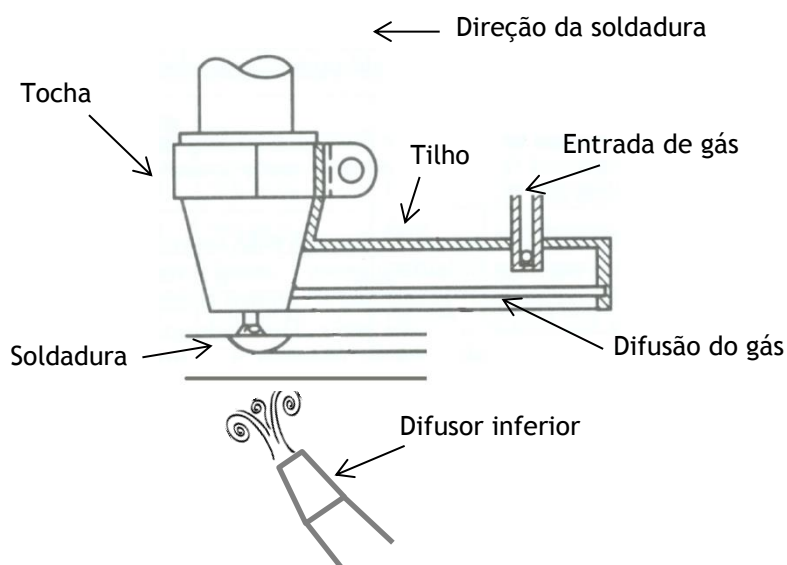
Proteção gasosa dos provetes de Ti-6Al-4V soldados por TIG
